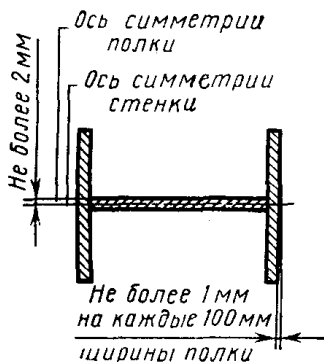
Допуски на сборку Н-образного сечения
